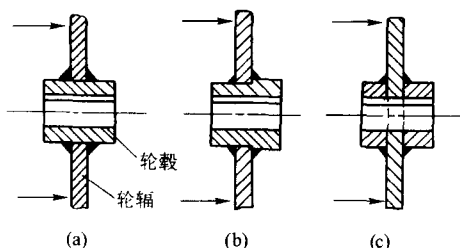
轮辐与轮毂的焊接接头设计
